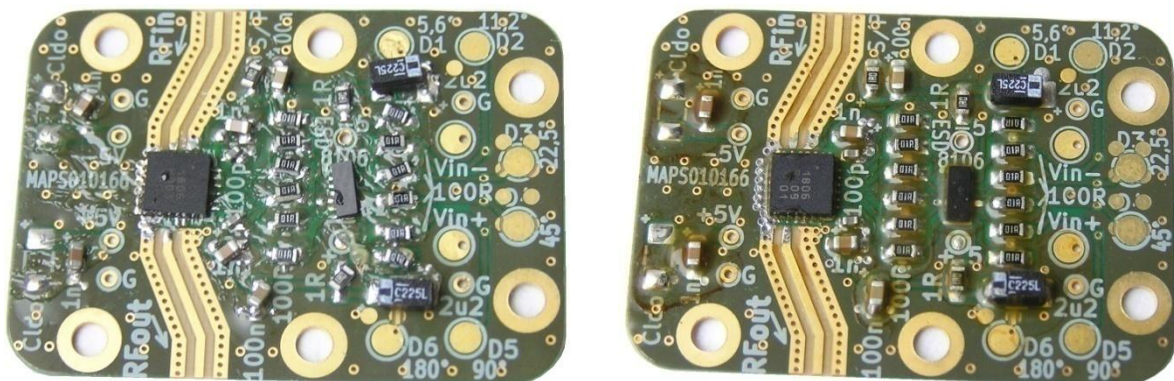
Hotový panel z JLC PCB (FR4, HASL)
